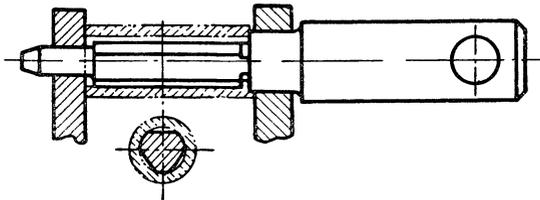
Штыри для установки деталей по внутренним цилиндрическим поверхностям.
